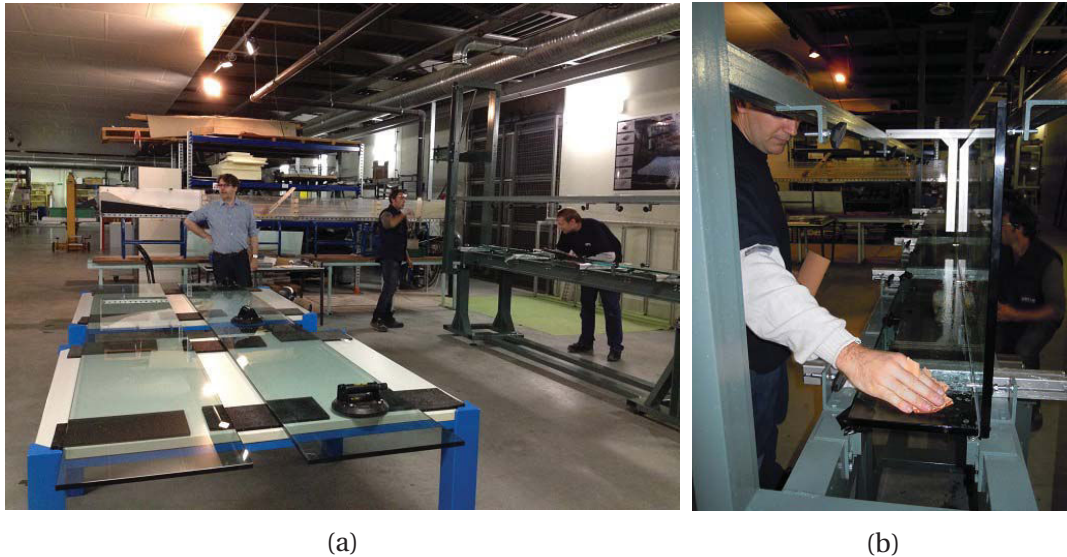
Collage des parois du canal en verre : (a) mise en position du fond; (b) collage d'une paroi vertical avec le fond.
